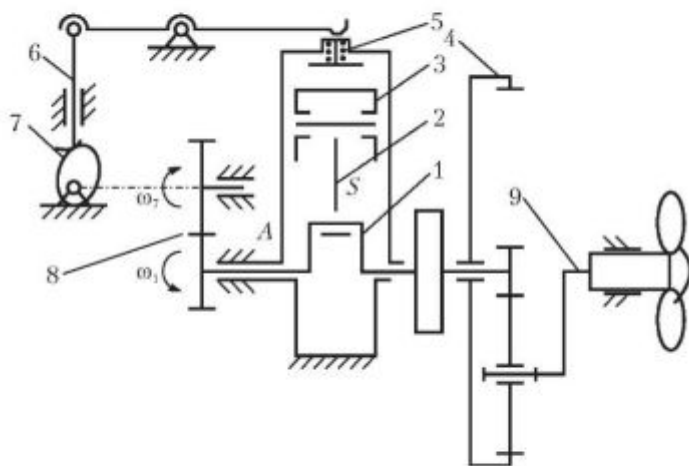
Структурная схема силового агрегата судового двигателя: 1 – коленчатый вал с маховиком, соединённый зубчатой передачей 8 с кулачковым валом 7; 2 – шатун; 3 – поршень, 4 – планетарный редуктор, 5 – клапан с пружиной, 6 – толкатель, соединённый рычагом с клапаном, 9 – винт
